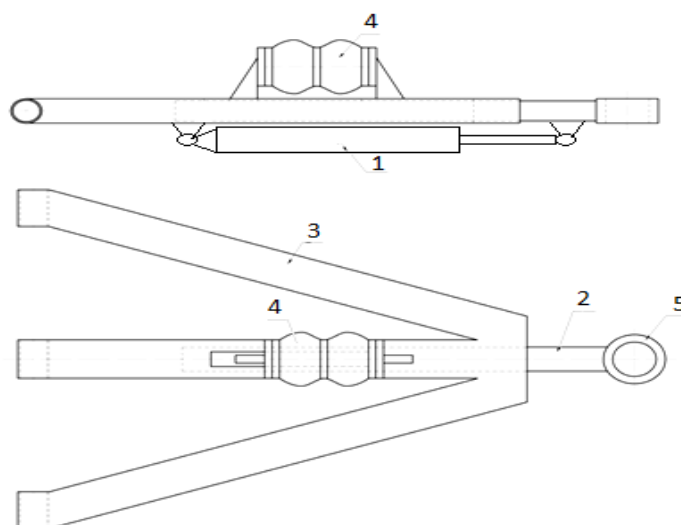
«Общий вид тягово-сцепного устройства с пневмокомпенсатором колебаний»
